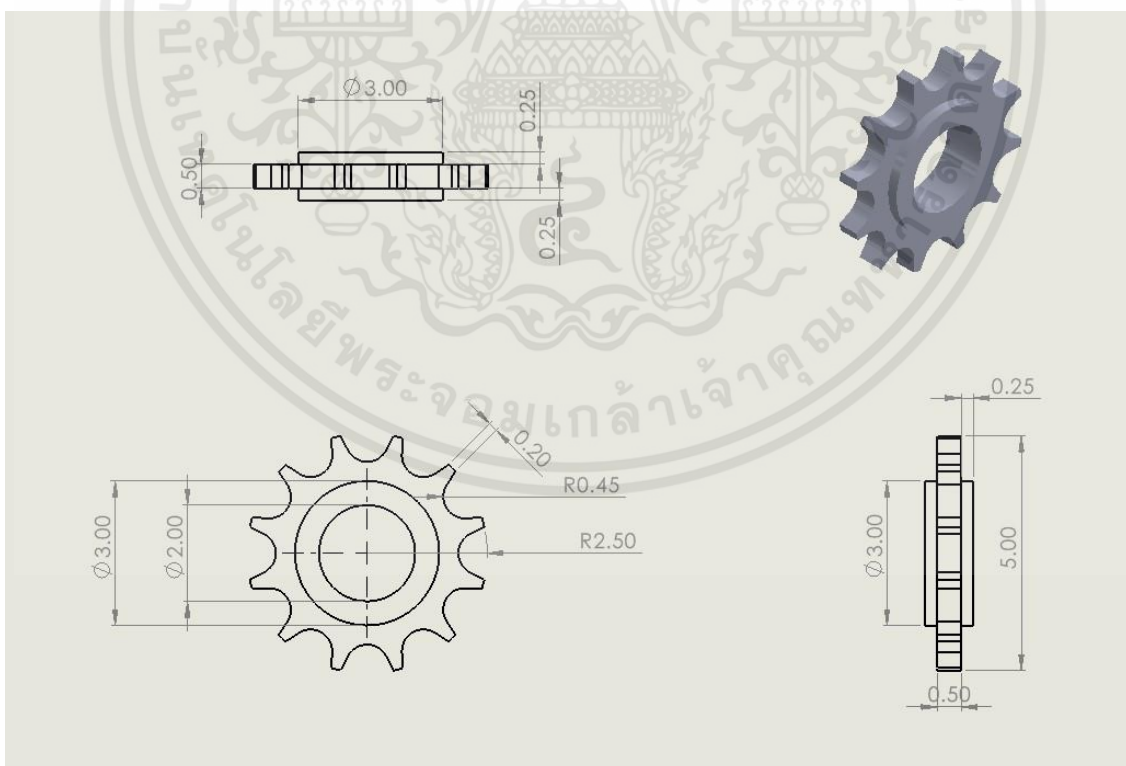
แบบโครงสร้างเครื่อง CAD
